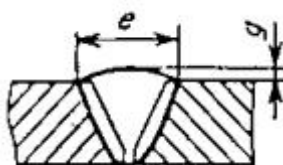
Конструктивные элементы сварного шва соединения С17 по ГОСТ-5284-80.
